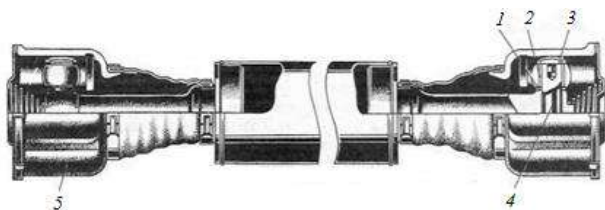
Карданний вал з двома універсальними шарнірами нерівних кутових швидкостей: 1 – два сферичних ролика; 2 – голчасті підшипники; 3 – заглушки; 4 – палець; 5 – корпус шарніра
